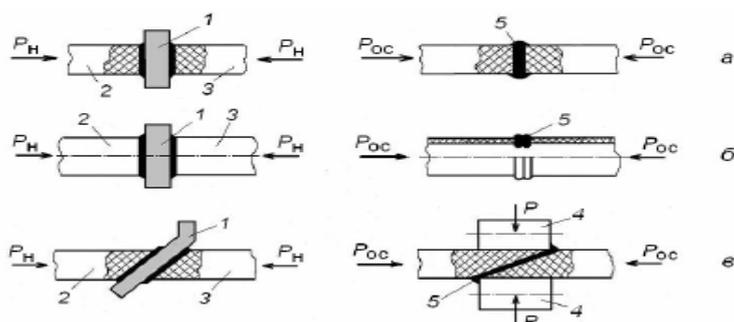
Схемы сварки прямым нагревом нагретым инструментом: а – сварка стержней встык; б – сварка труб встык; в – сварка соединения «на ус»: 1 – нагретый инструмент; 2, 3 – свариваемые детали; 4 – прижимные ролики; 5 – сварной шов; слева – нагрев; справа – осадка; P_H – давление при нагреве; P_{OC} – давление при осадке
